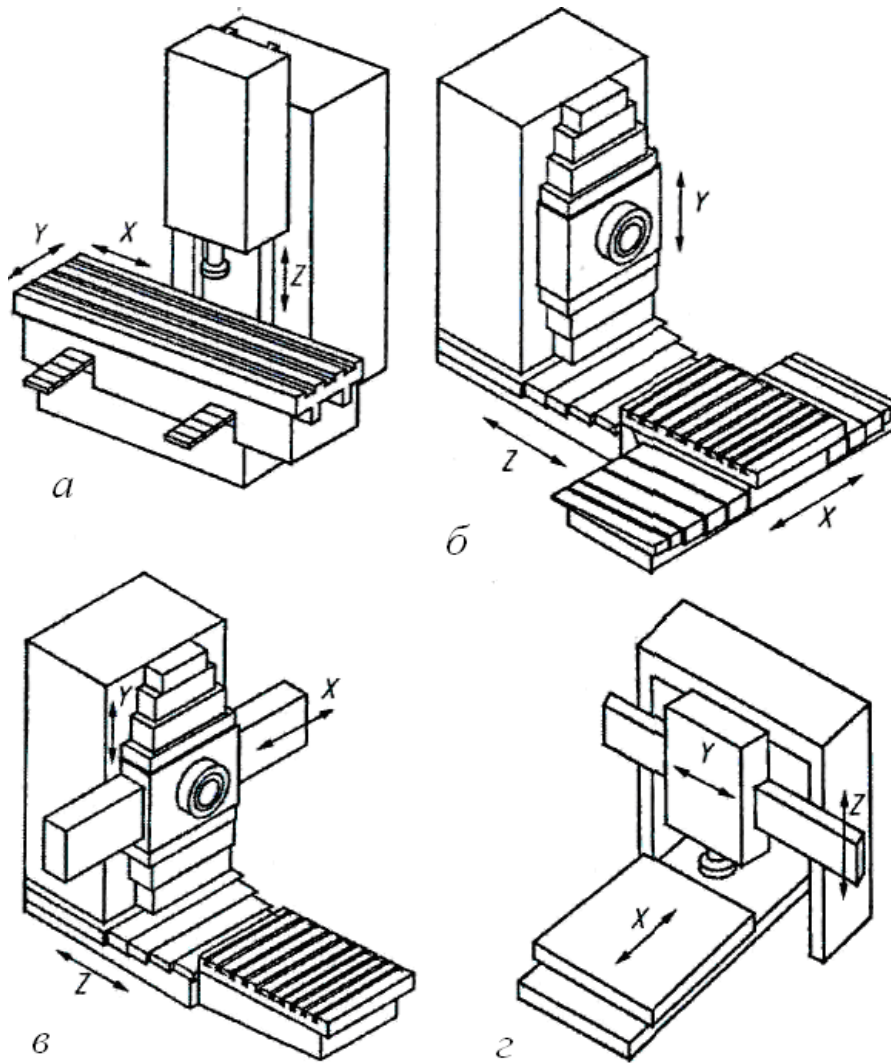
Компонувочные схемы станков сверлильно-фрезерно-расточной группы:
